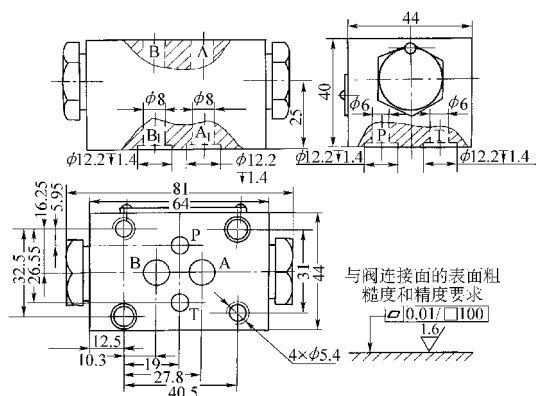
Z2S-6 型叠加式液控单向阀的外形尺寸
